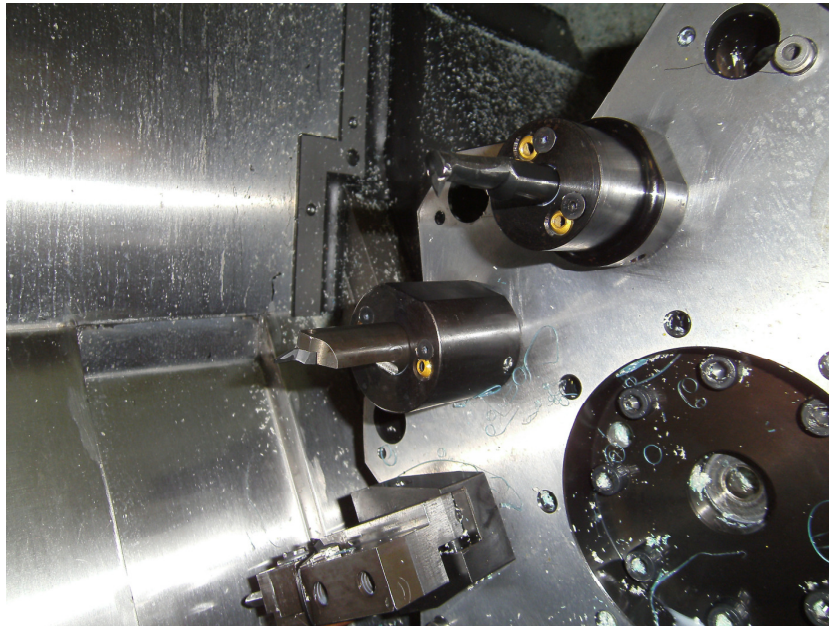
Spinner C 400/52 mit Werkzeugen
